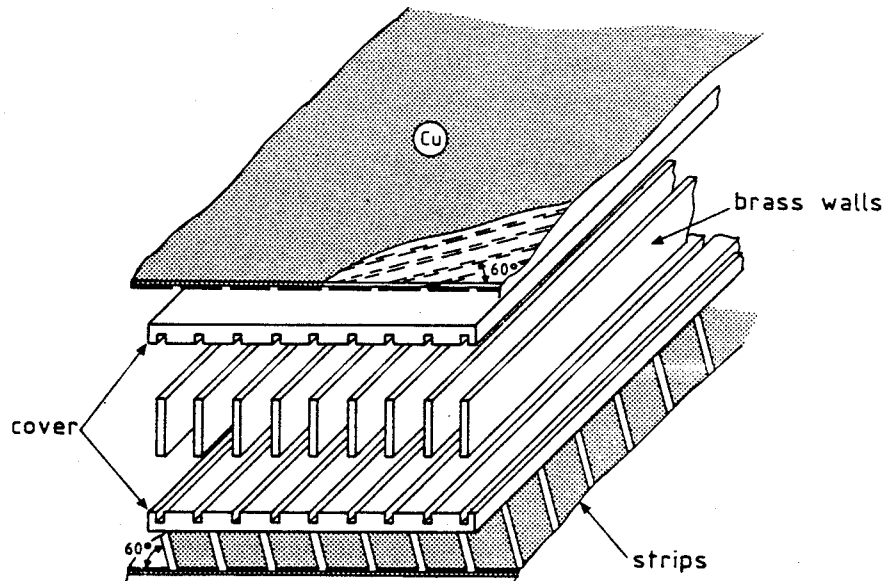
Die Explosionszeichnung einer Kammer mit Messingwänden
